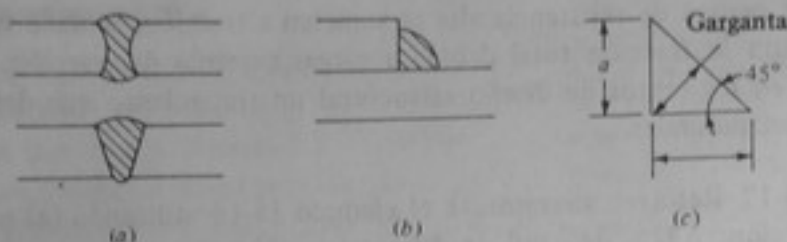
(a) Soldaduras a tope. (b) Soldadura con filete. (c) Sección transversal neta de la soldadura con filete.
